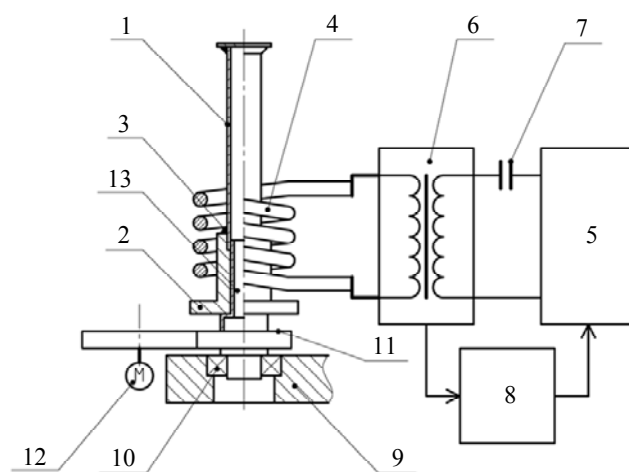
Схема устройства для индукционной пайки гильз-держателей: 1, 2 – детали гильзы-держателя; 3 – припой; 4 – индуктор; 5 – генератор электрической мощности; 6 – трансформатор; 7 – конденсатор; 8 – автогенератор; 9 – опора; 10 – подшипниковый узел; 11 – поворотная платформа; 12 – привод; 13 – посадочное место
